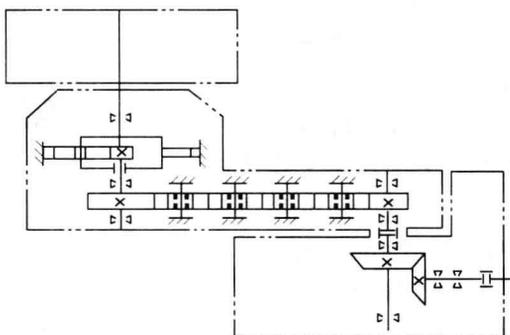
圆锥—圆柱齿轮—行星齿轮传动
